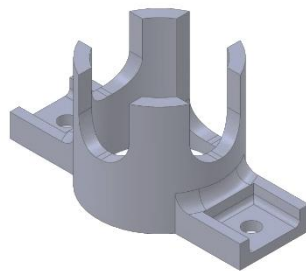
Desenho 3D do suporte do motor elétrico da pá misturadora.
